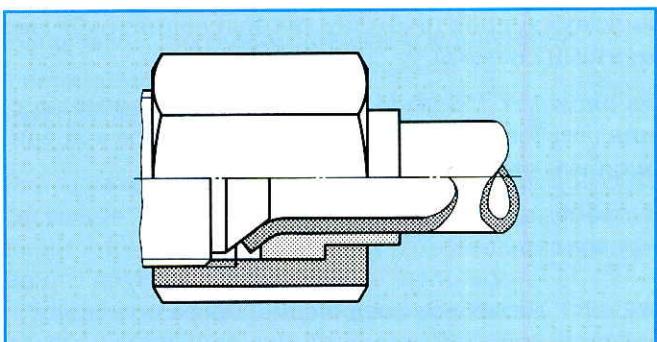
Резьбовое соединение с уплотняющей отбортовкой. Уплотнение: металл по металлу. Фиксация осуществляется при помощи отбортовки под углом 37°, прижимаемой к проточке на штуцере.
